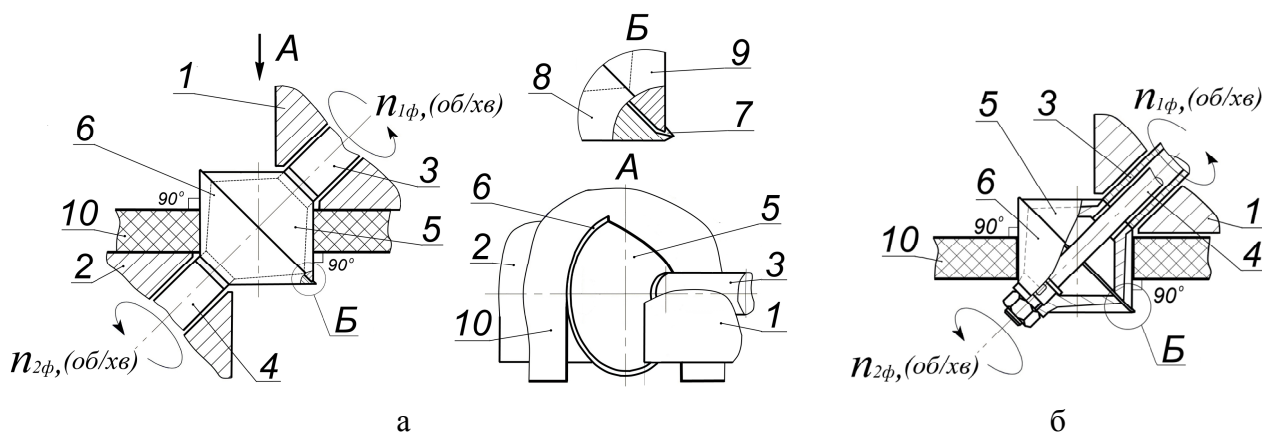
Пропонований пристрій для механічного розрізання виробів листової форми із ВПКМ: а – з двома корпусами; б – з одним корпусом
